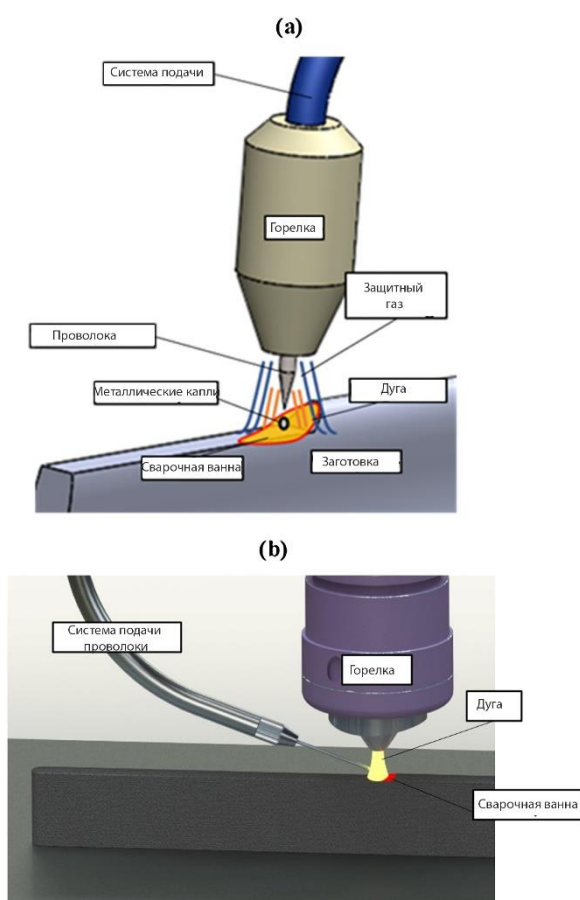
Графическое изображение: (а) процесса сварки неплавящимся электродом (GTAW) и (б) процесс плазменно-дуговой сварки (PAW)
